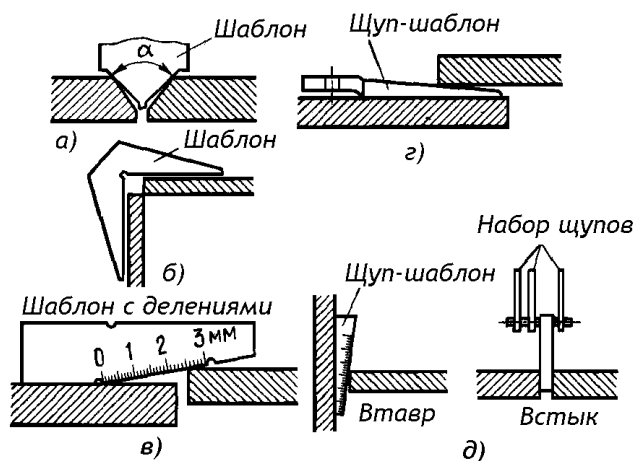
Инструмент для проверки качества сборки, где а – угла раскрытия листов; б – правильности прямого угла сборки; в – величины превышения кромок; г – зазора между листами в нахлестку; д – зазоров при соединении в тавр и в стык
